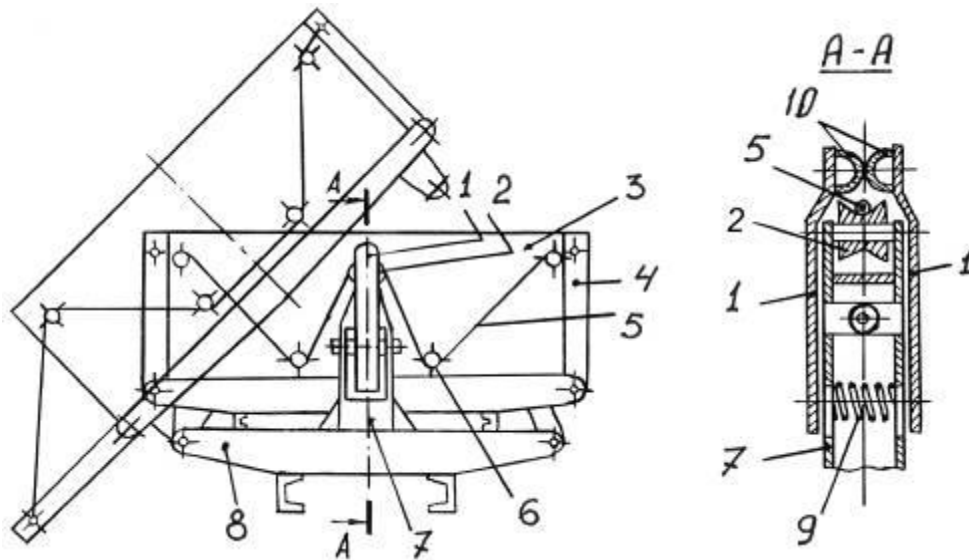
Пристрій для примусового закривання бокового борту платформи самоскида:
